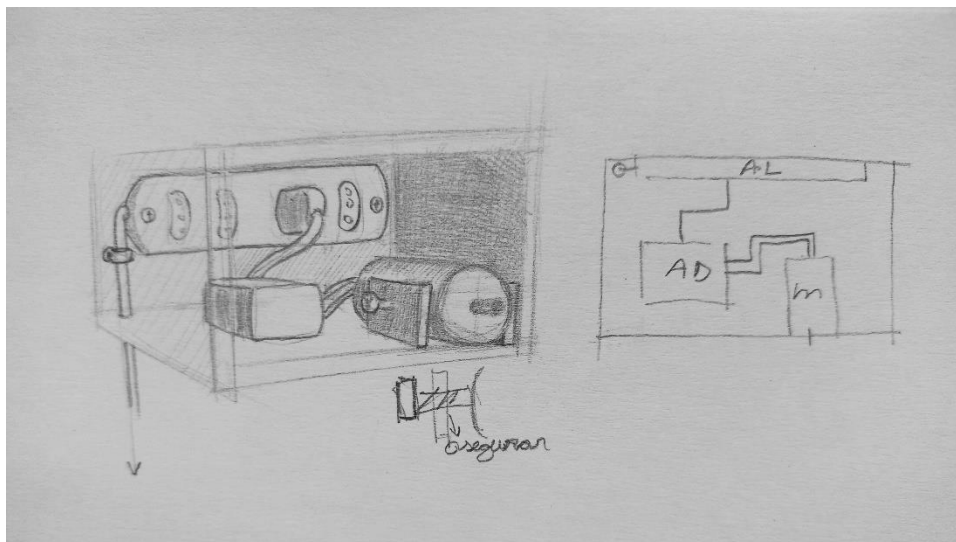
Croquis que describe el módulo que utilizarán las máquinas.
